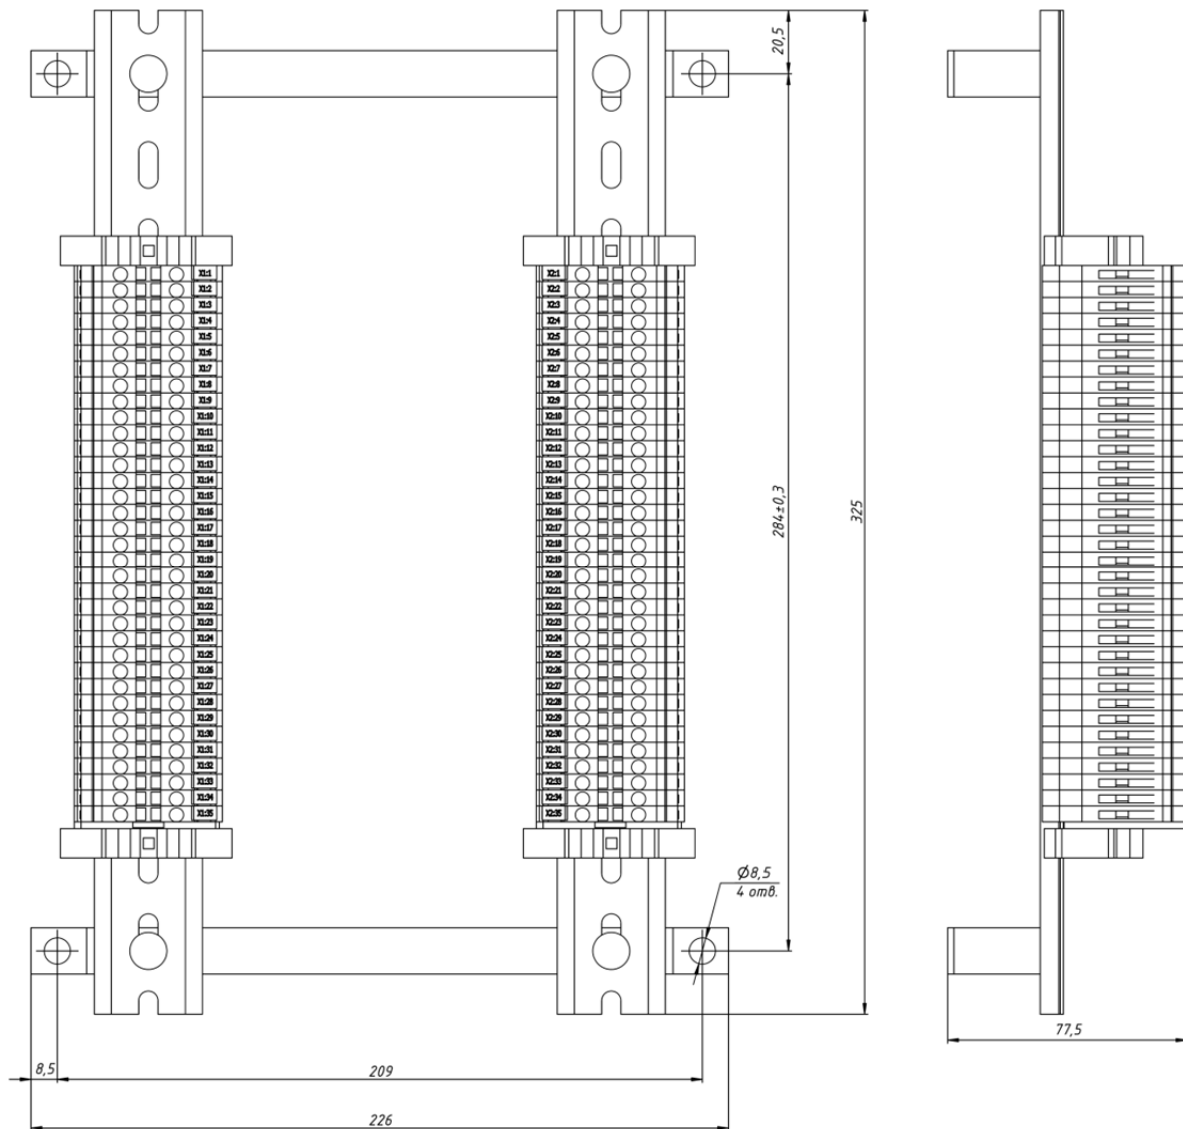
Габаритные размеры рейки с клеммниками.
